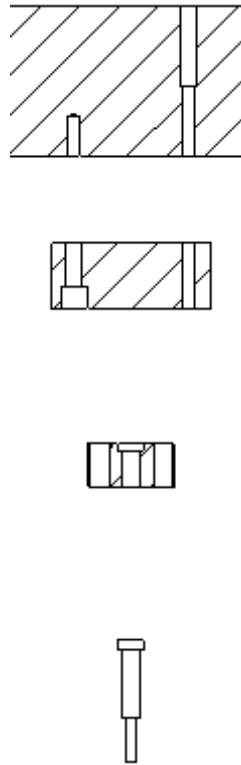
Imagem de corte da montagem dos componentes da parte superior da ferramenta que permitem obter o corte de referência B.
